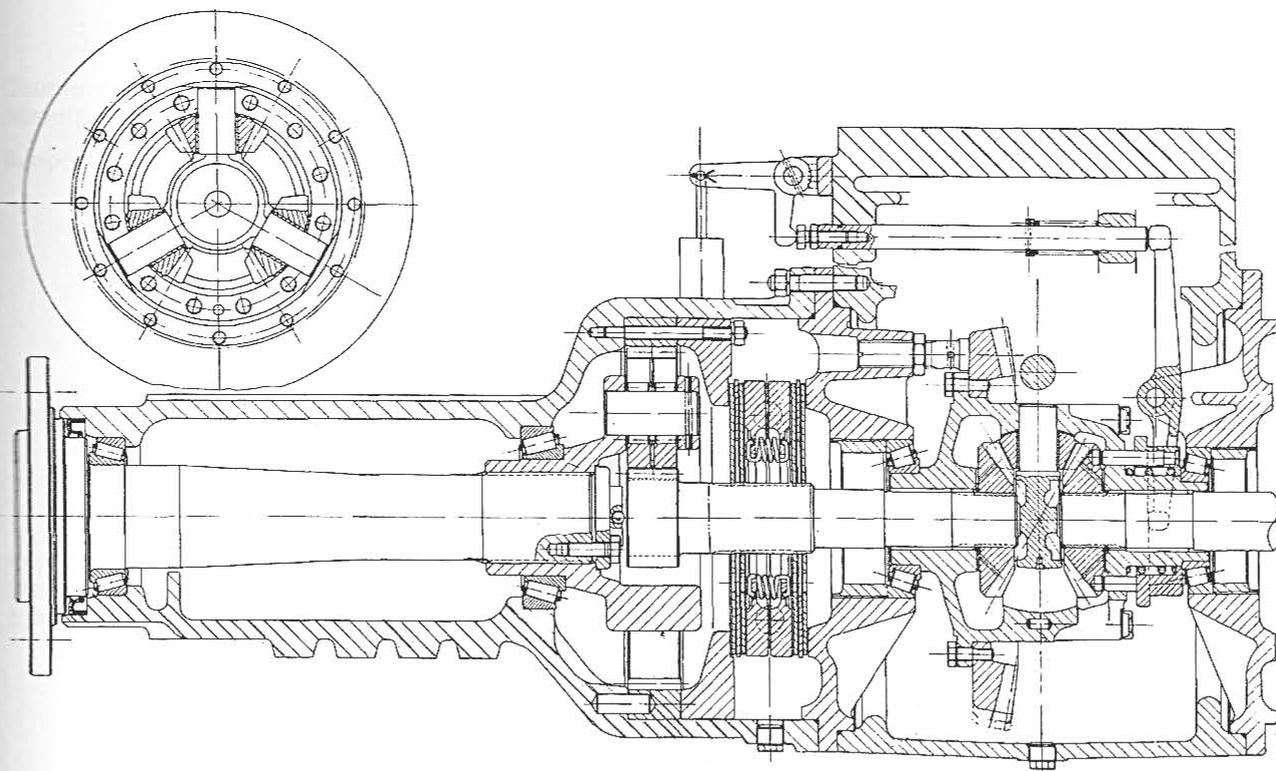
Coupe transversale arriere des tracteurs R 904
